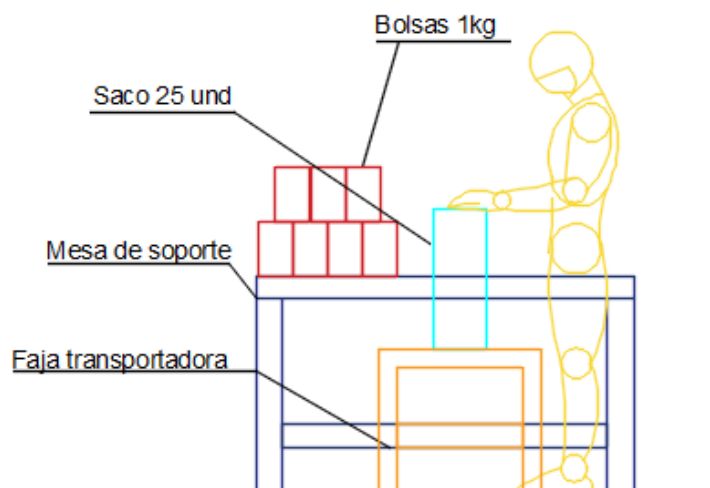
Puesto de labores de empaquetado – Vista lateral propuesta
